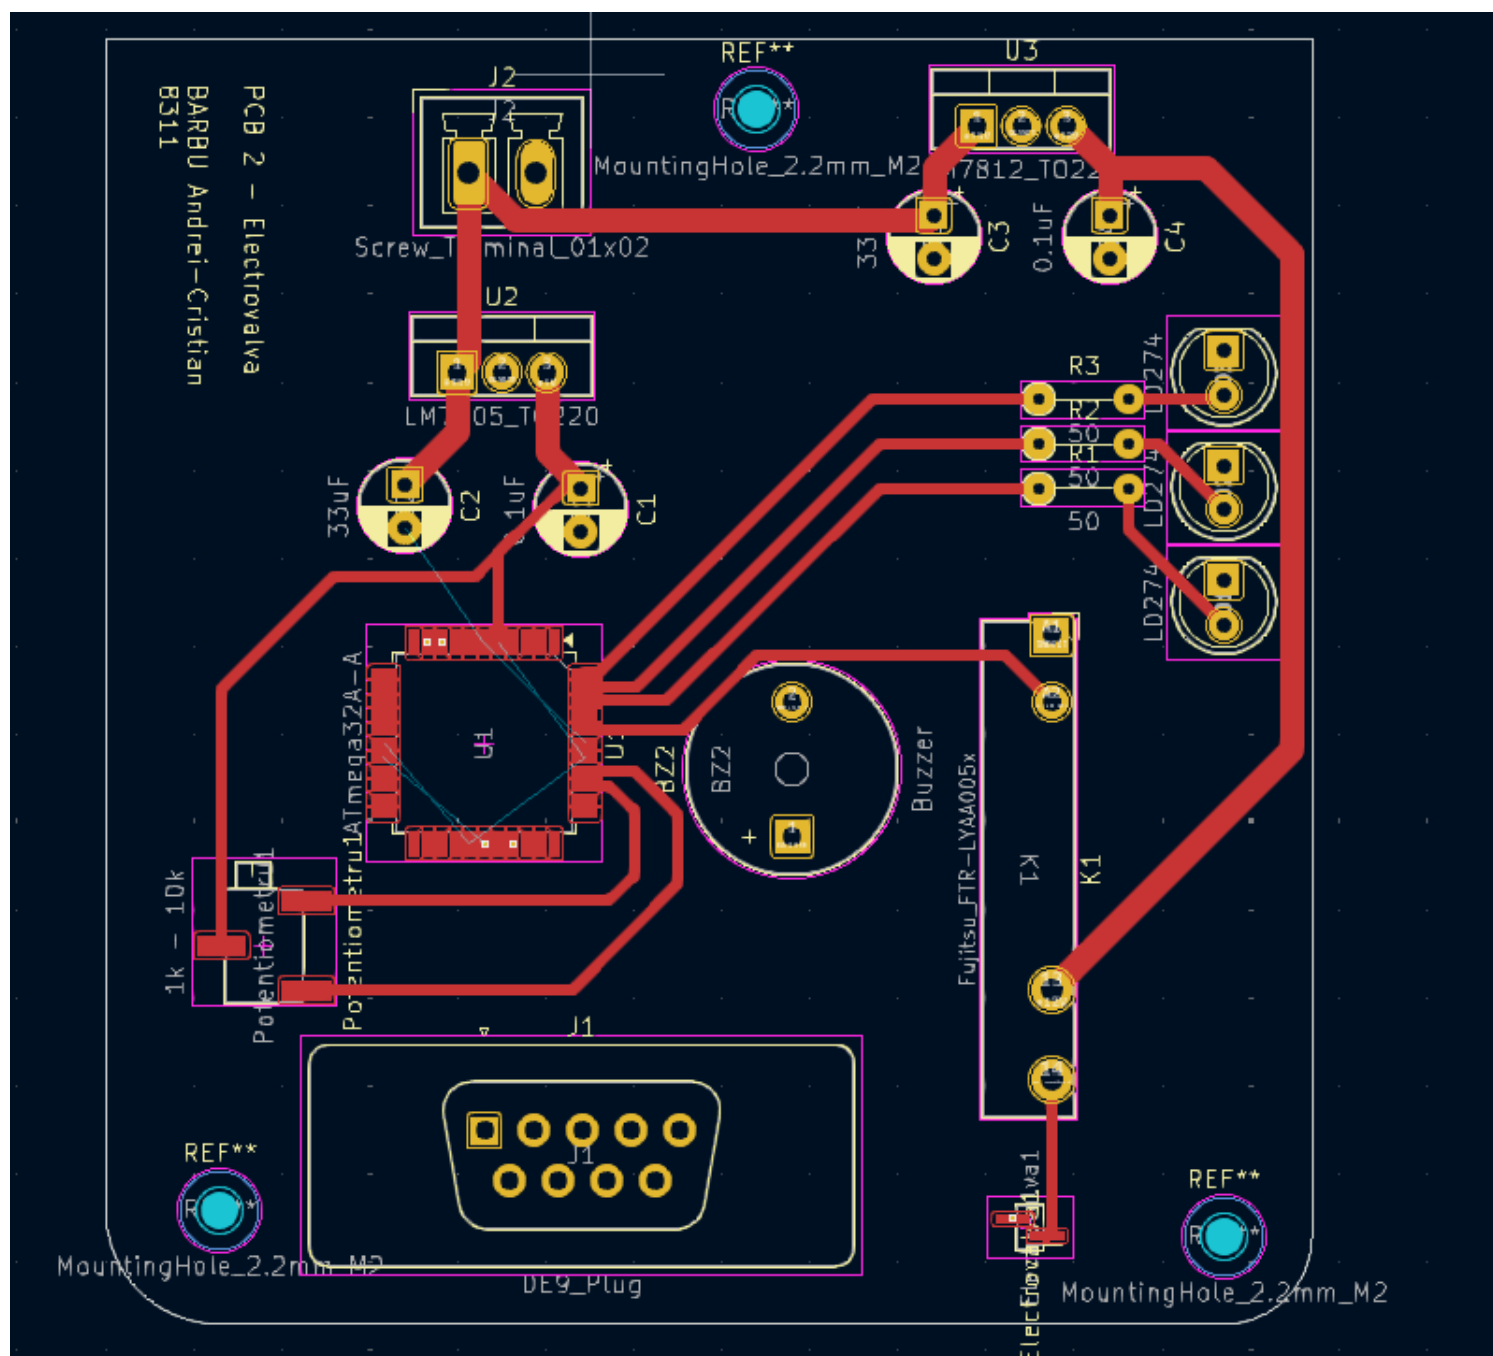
Cablaj imprimat din KiCad (Front Layer)
